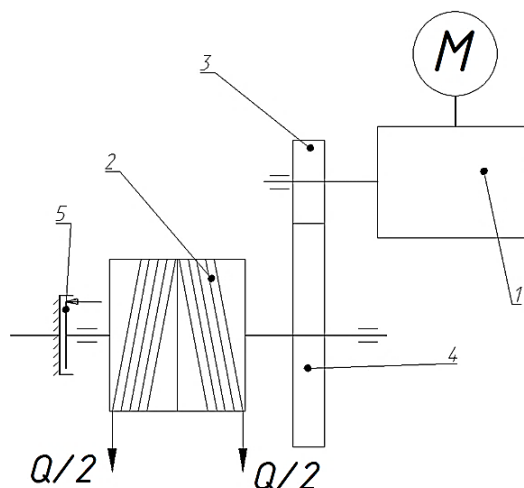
Кинематическая схема привода подъема телекамеры модернизированной ТВШ: 1 – цилиндро-червячный мотор-редуктор; 2 – барабан; 3 – шестерня; 4 – зубчатое колесо; 5 – тормозное устройство [Kinematic diagram of the lift drive for an upgraded TVSH: 1 - helical-worm gearmotor; 2 - drum; 3 - gear; 4 - gear wheel; 5 - braking device]
